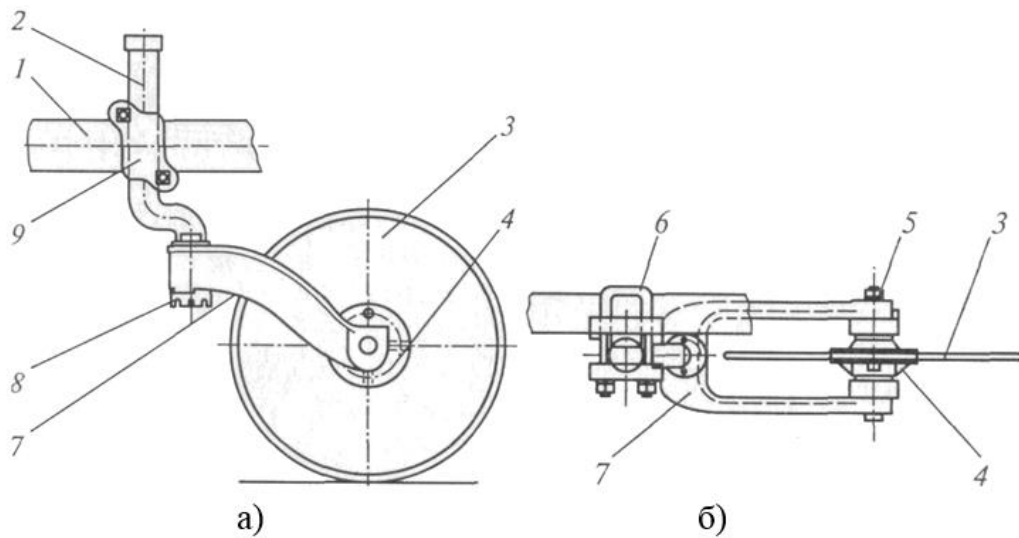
Дисковий ніж: а) – вид з боку; б) – вид зверху; 1 – рама плуга; 2 – стійка; 3 – диск; 4 – ступиця; 5 – вісь; 6 – скоба; 7 – вилка; 8 – корончата гайка; 9 – державка
